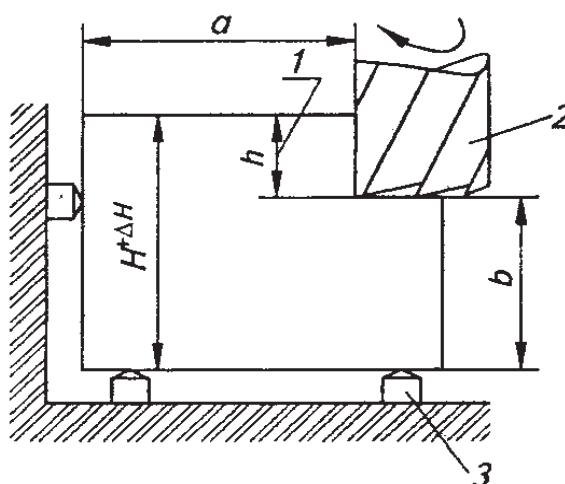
Схема установки заготовки при фрезеровании уступа: 1 – высота уступа; 2 – фреза; 3 – опорные точки
